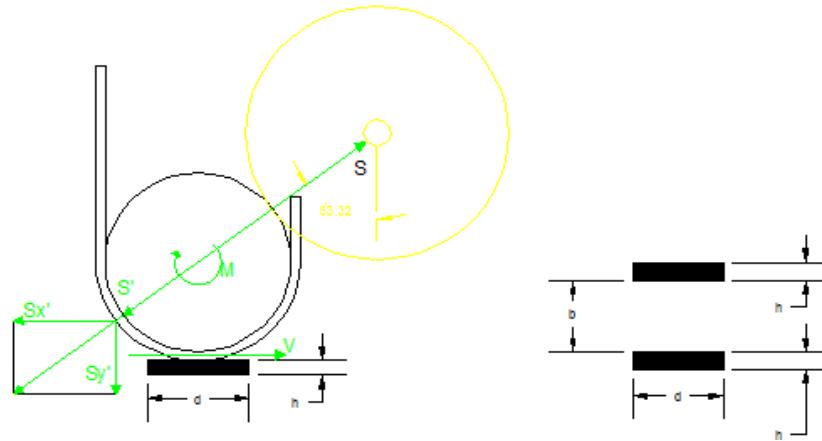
Vista frontal e inferior del gancho soldado en la cadena
